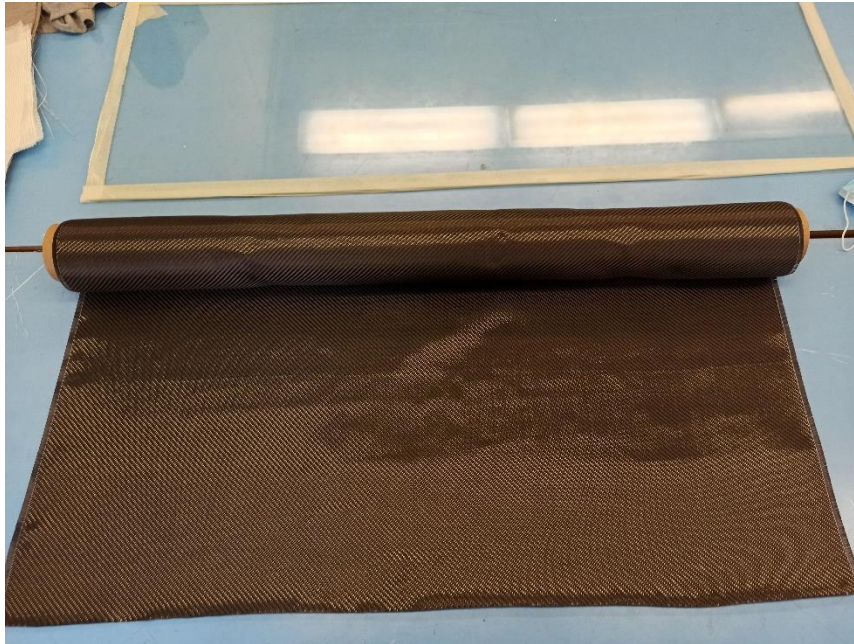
Sklenená tabuľa ktorá slúži ako forma oblepená papierovou páskou.
